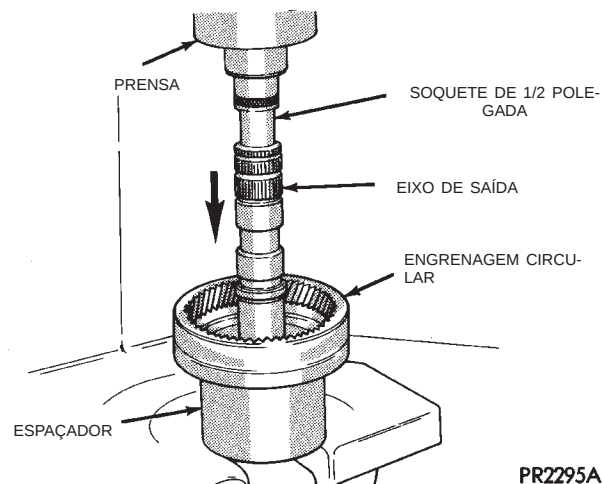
Instalação do Eixo de Saída na Engrenagem Traseira Circular com Dentes Interiores
